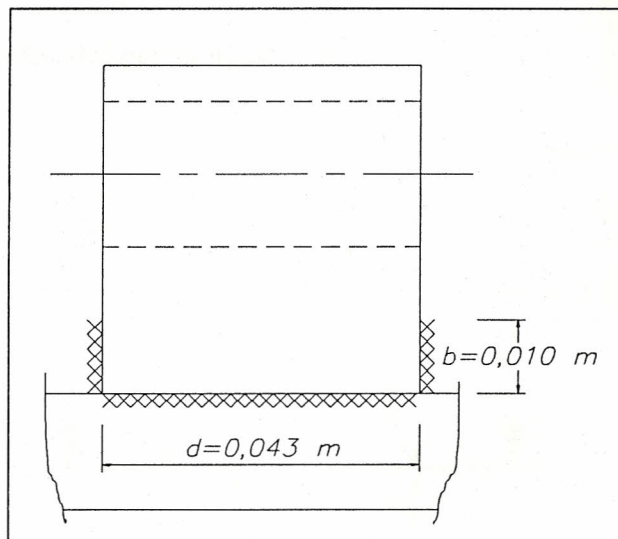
Esquema de las dimensiones del cordón de soldadura.
